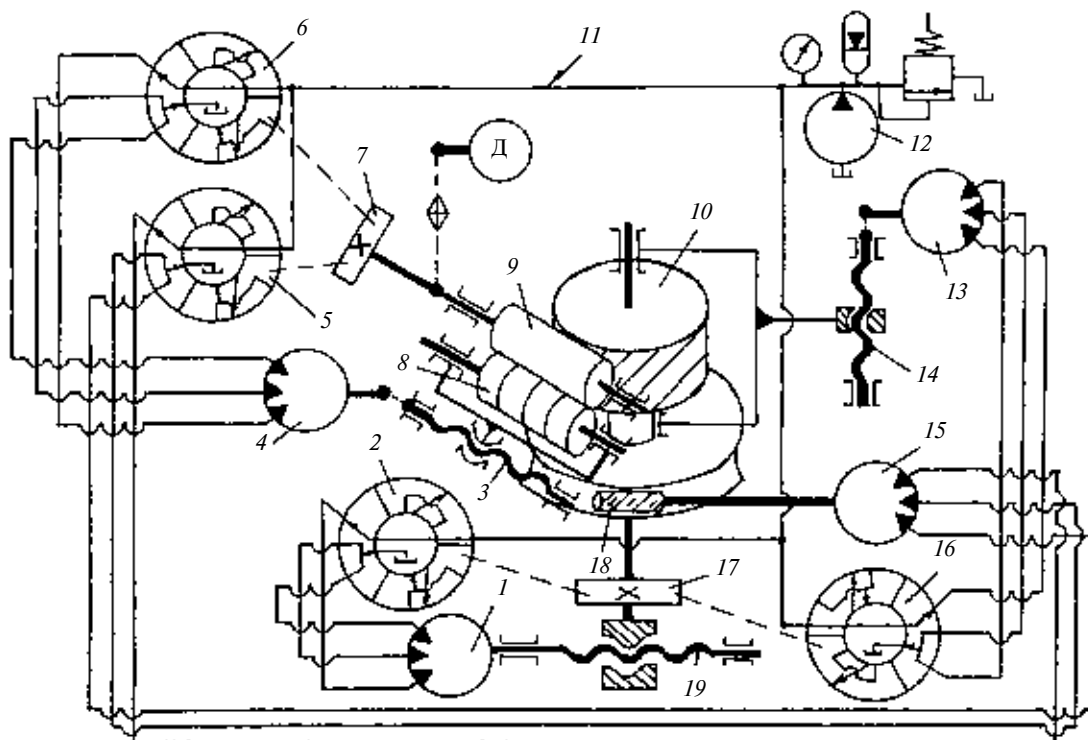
Структурная схема зубошлифовального станка с гидравлическими связями во внутренней цепи для шлифования зубьев цилиндрических зубчатых колес абразивным червяком:
